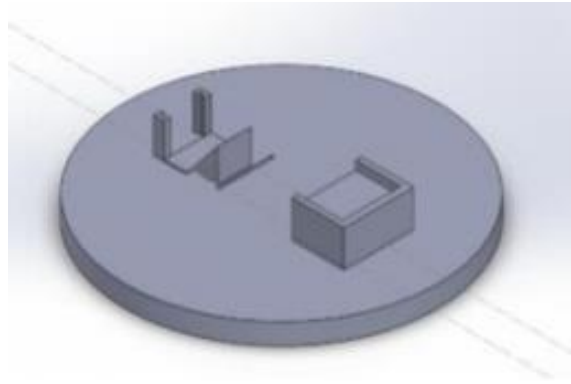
Segunda propuesta de Fixture, vista Isométrica.
